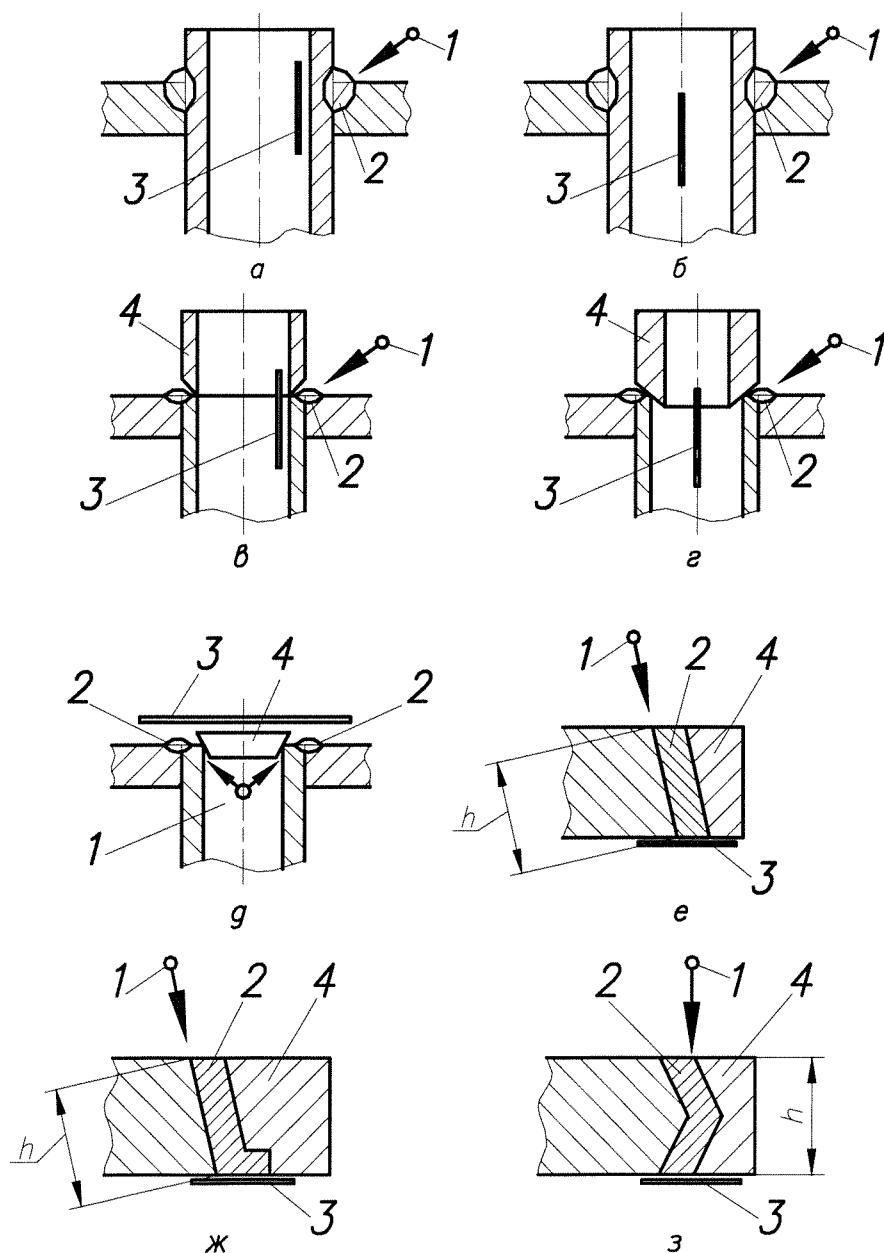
(а-з), - Схемы контроля сварных соединений вварки труб в трубные доски (а-д) и схемы контроля наплавки (е-з): 4 - приставка-компенсатор; остальные обозначения см. рис. 5.2
